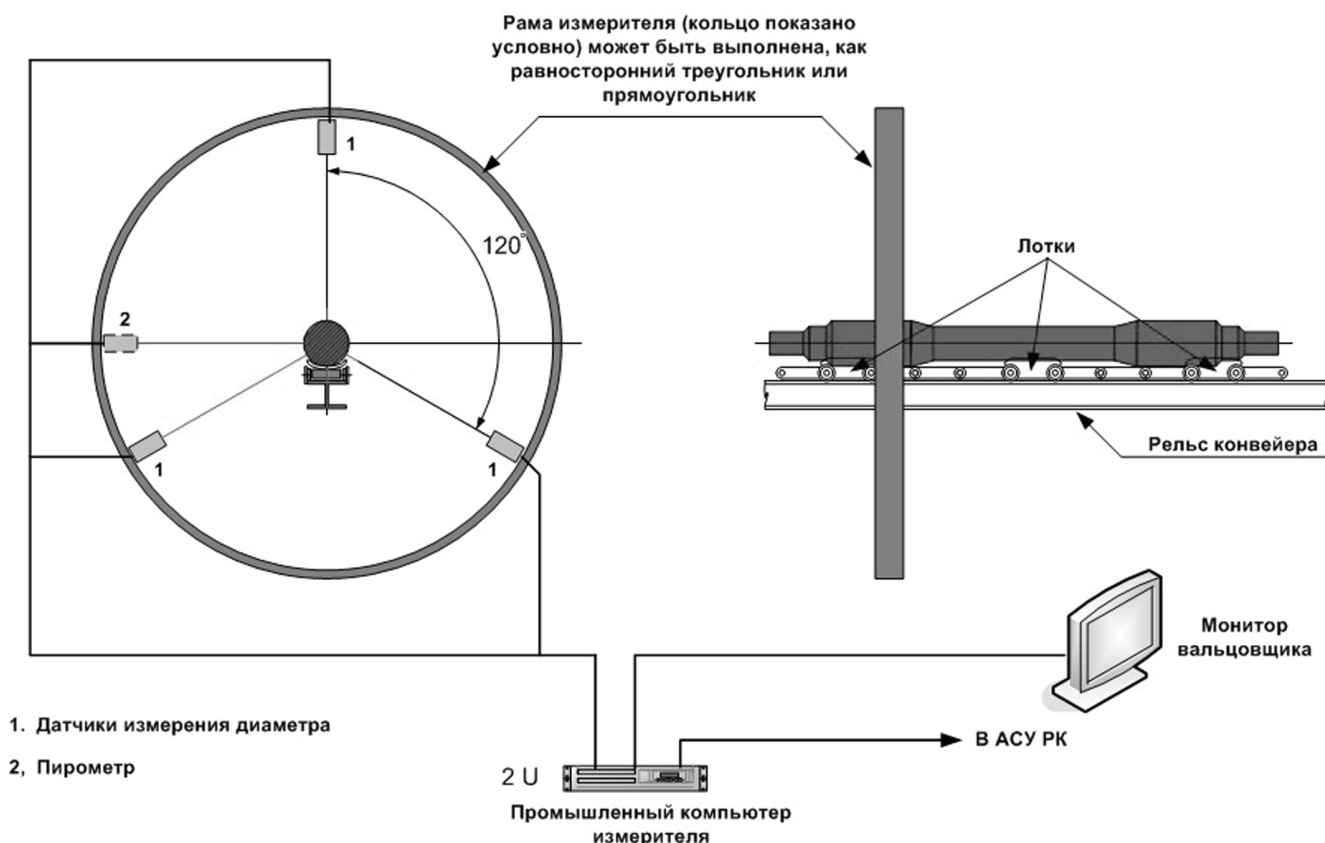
Схема измерения геометрических размеров осевой заготовки
